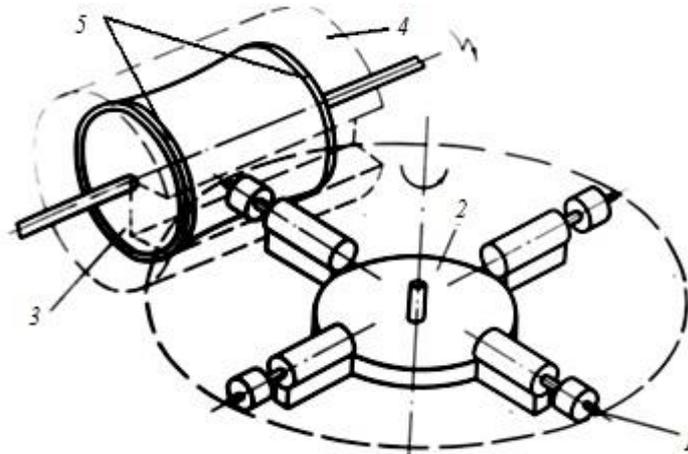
Схема исследований: 1 - образец; 2 - крестовина;
